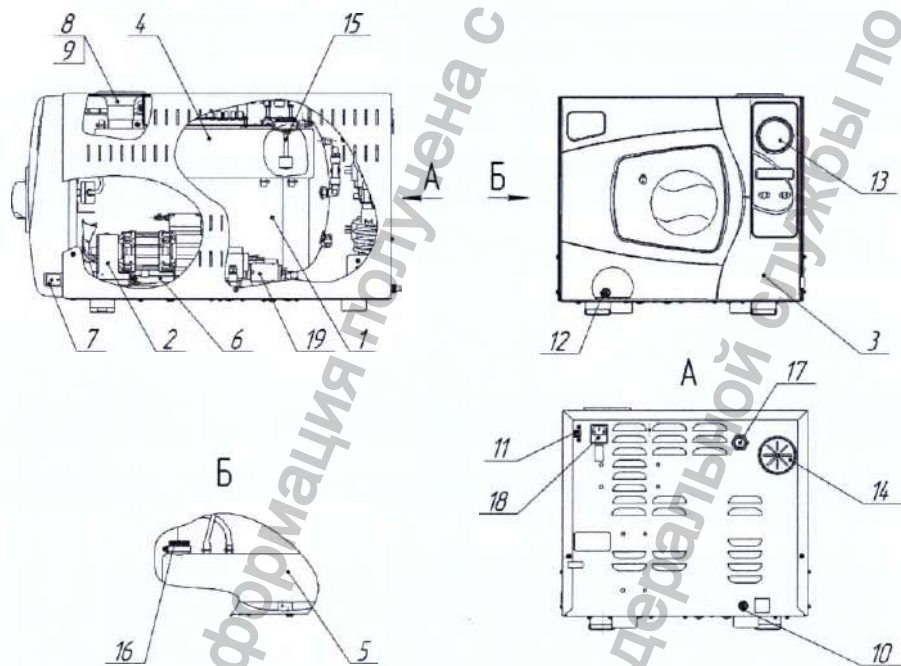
Внешний вид стерилизатора парового ГКа-25-ПЗ в варианте исполнения КИУС.942711.004-05:
